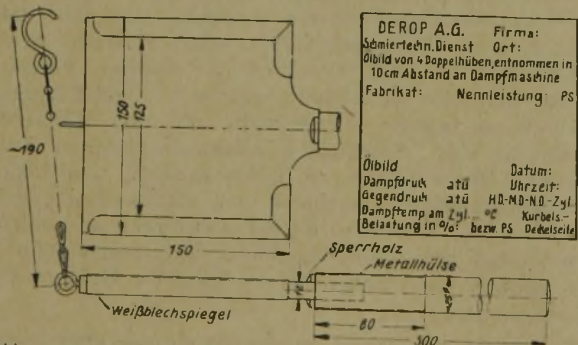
Ölbildnehmer und -karte für Kolbenmaschinen
